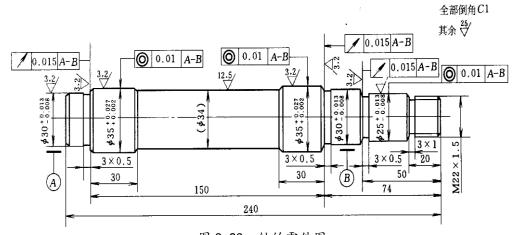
轴的零件图 表 8-8 轴的车削工艺过程
